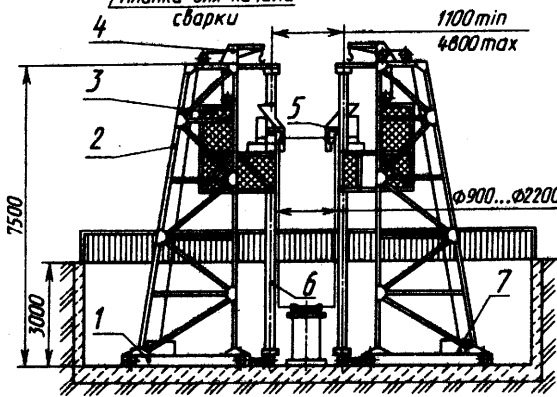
Установка для электрошлаковой сварки продольных швов
